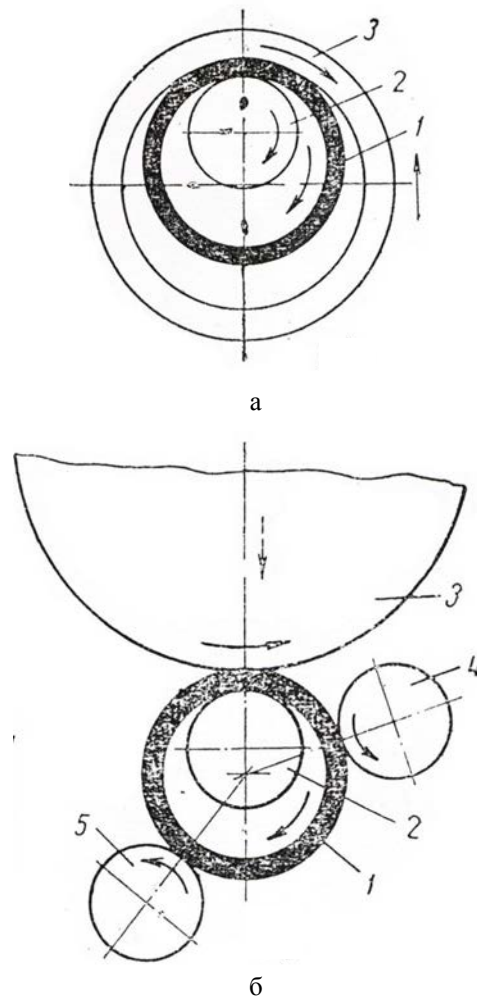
Закрытый (а) и открытый (б) способы раскатки колец
